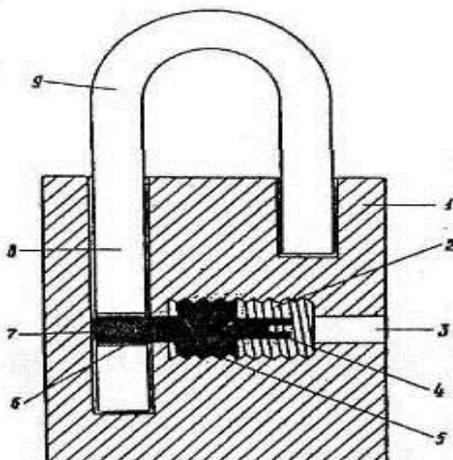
Устройство винтового замка: 1 — корпус; 2 — отверстие в корпусе для засова; 3 — отверстие для ключа; 4 — хвостовик засова; 5 — винтовой засов; 6 — отверстие в запираемом конце дужки; 7 — головка засова; 8 — запираемый конец дужки; 9 — дужка
